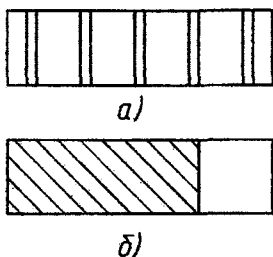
Примеры рельефа реек: а) для накатывания детали со шлицами; б) для накатывания резьбы
